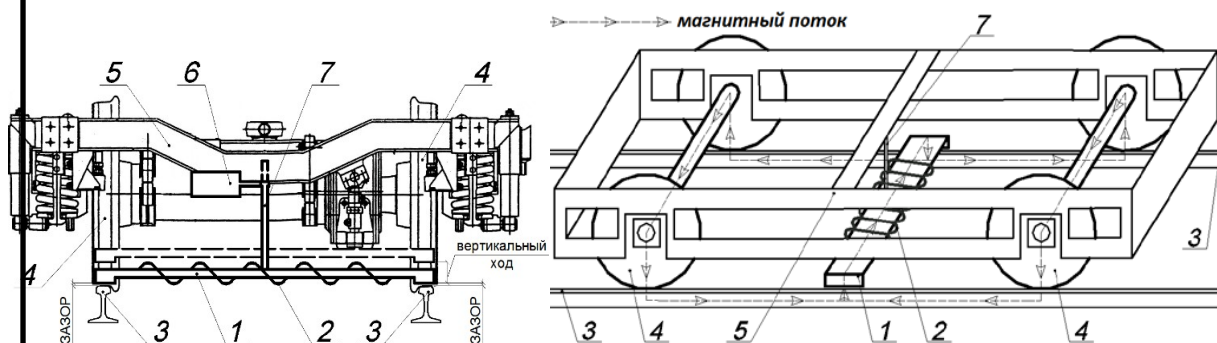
Схема розташування індуктора між колісними парами над рейками: 1 – магнітопровід; 2 – котушка; 3 – рейка; 4 – колесо; 5 – рама візка; 6 – електродвигун; 7 – немагнітна зубчаста рейка
